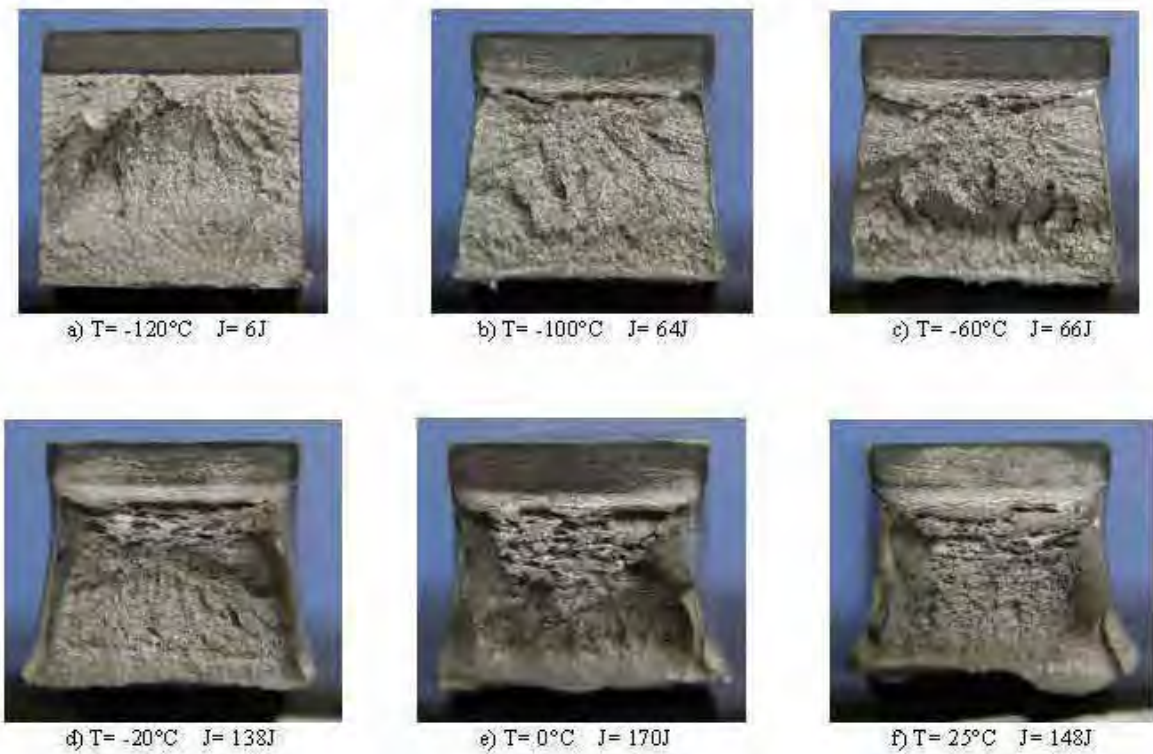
Fractografia da superfície de fratura do aço A516-R23 °C/s, corpo-de-prova entalhado.
